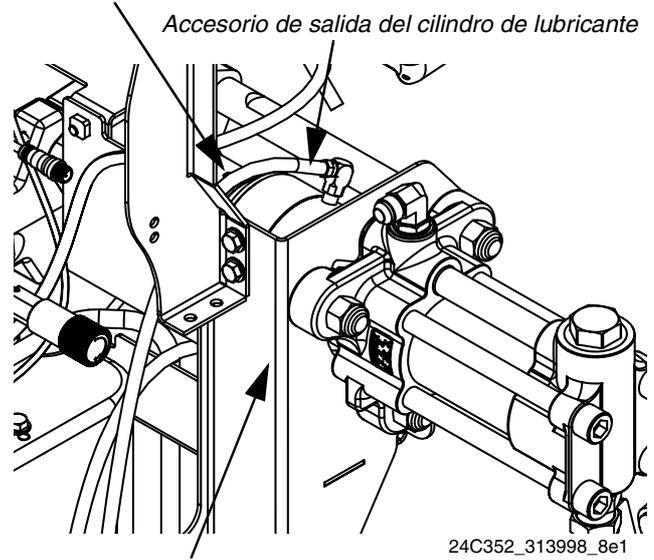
Cilindro de lubricante, visto desde la parte trasera izquierda de la máquina.
